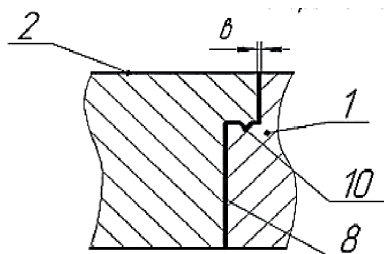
Вариант установки основания в корпусе матрицы: 1 – корпус матрицы; 2 – основание; 8 – зазор; 10 – выступ; b – ширина температурного зазора
